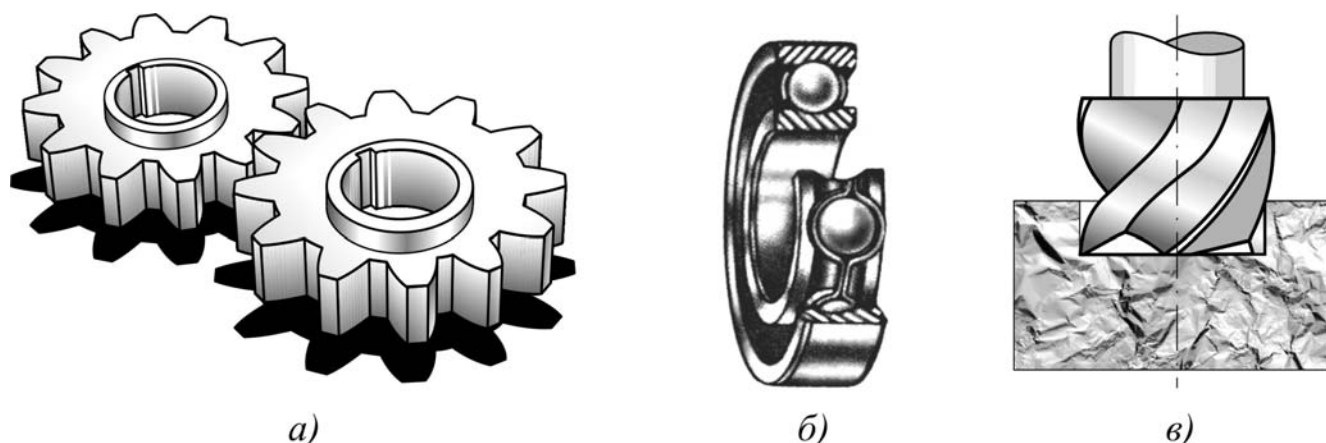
При решении контактной задачи массивами представляют, например, зубья цилиндрических, конических и червячных зубчатых передач – а); тела качения и беговые дорожки подшипников качения – б); торцевую фрезу и обрабатываемый материал – в)
